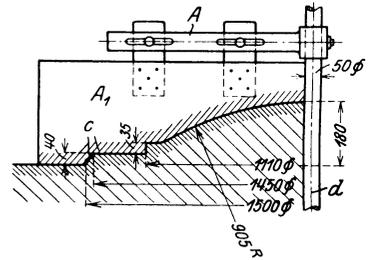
„Falsches Bett“ für Oberkasten zu Fig. 111.
